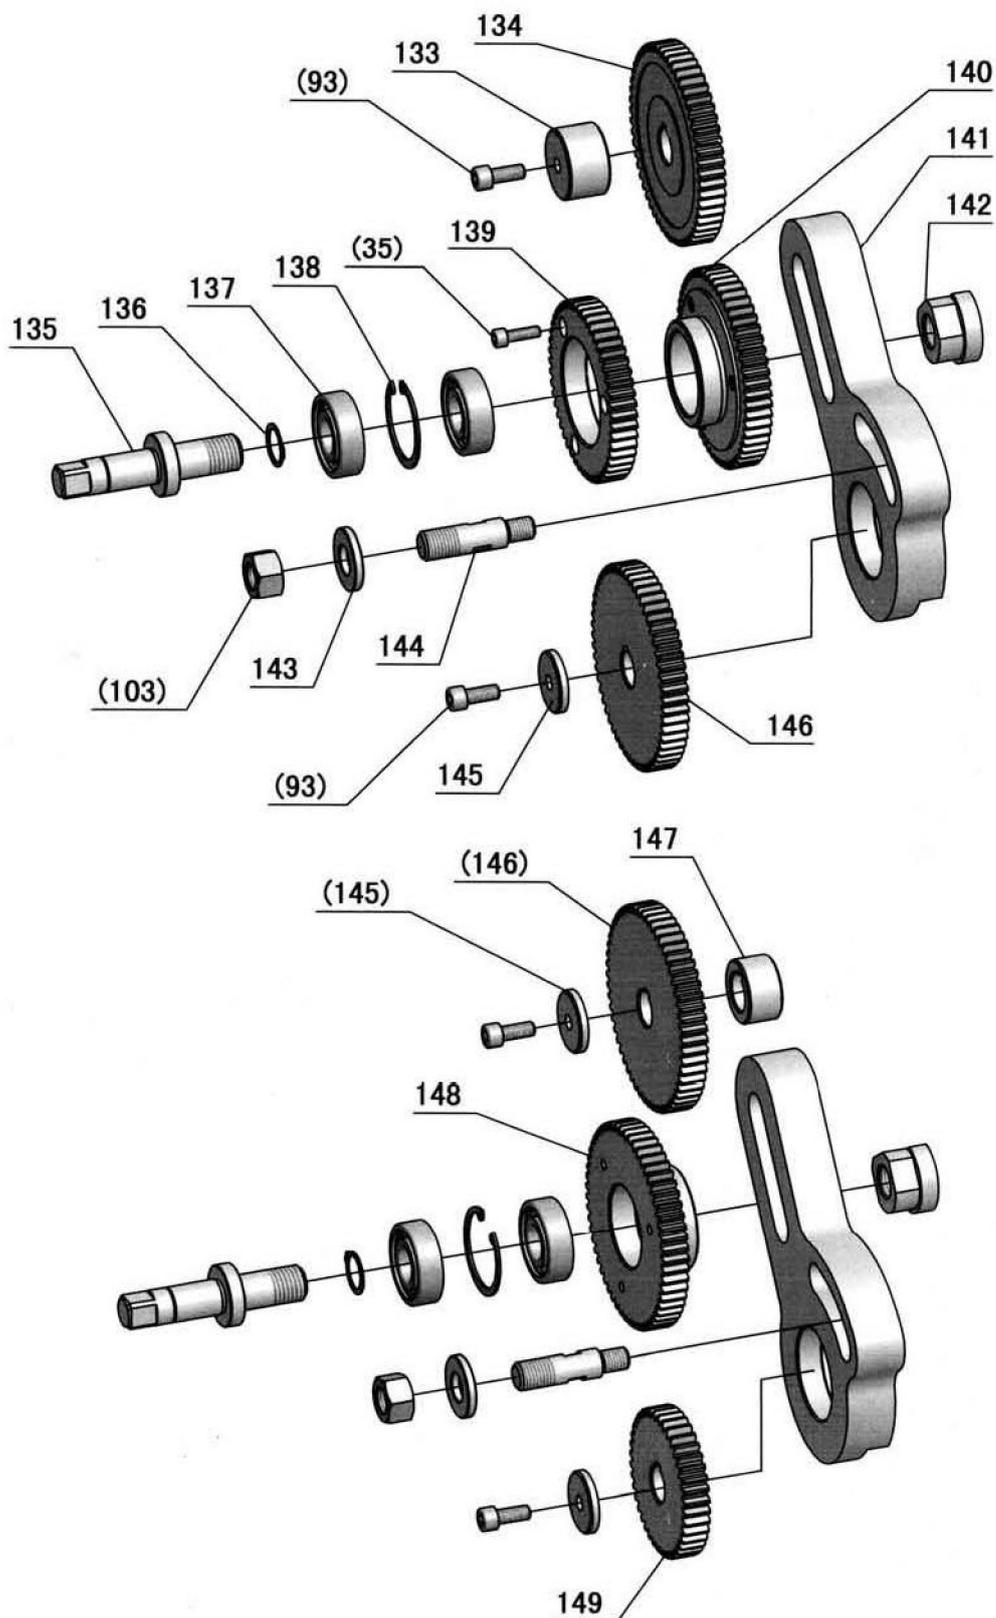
Wechselradgetriebe (metrisch) – Cambio engranaje rueda (métrico)
